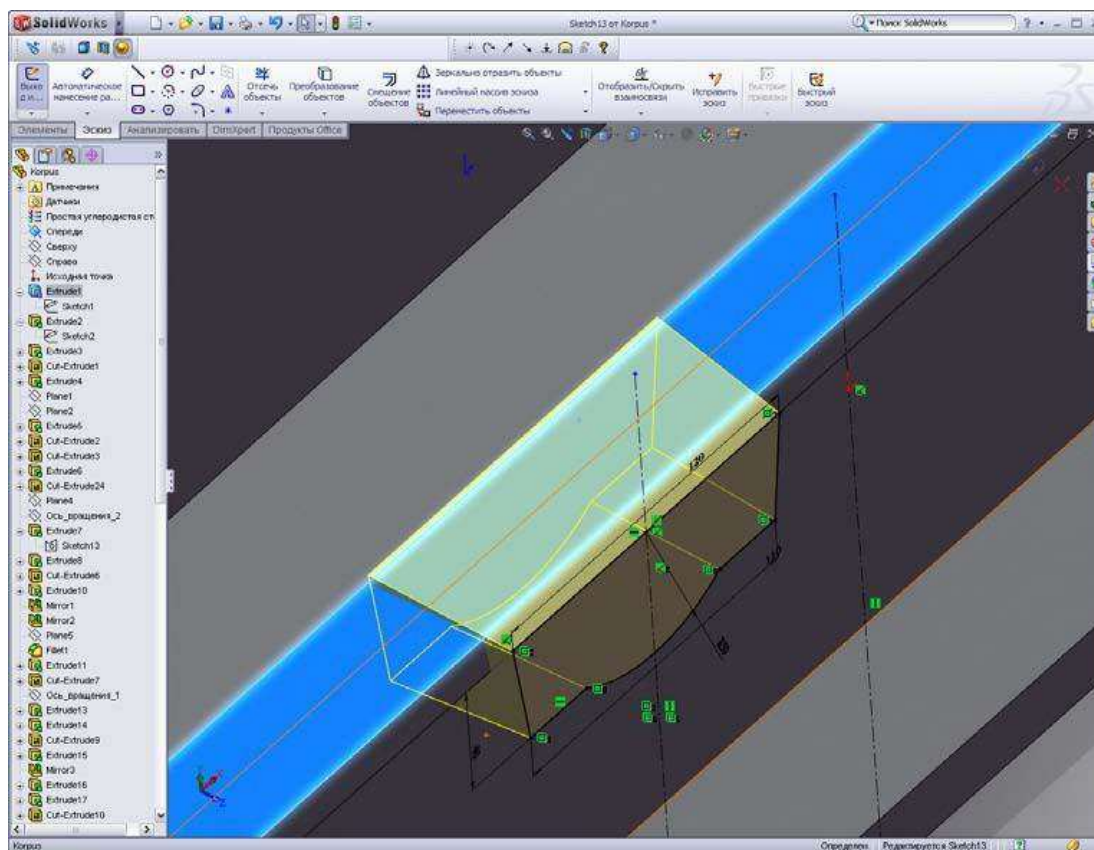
Редагування ескізу бобишки на площині стінки деталі корпусу
